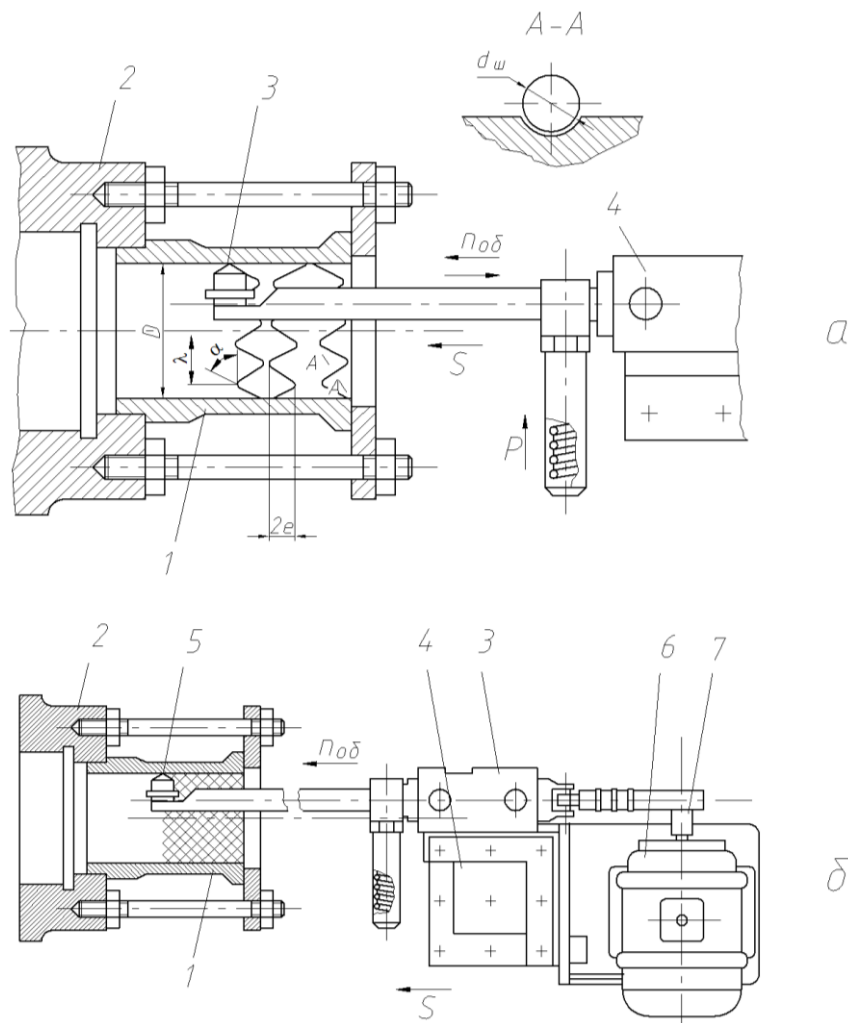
Схема обкочування поверхні циліндра сталлюю кулькою:
